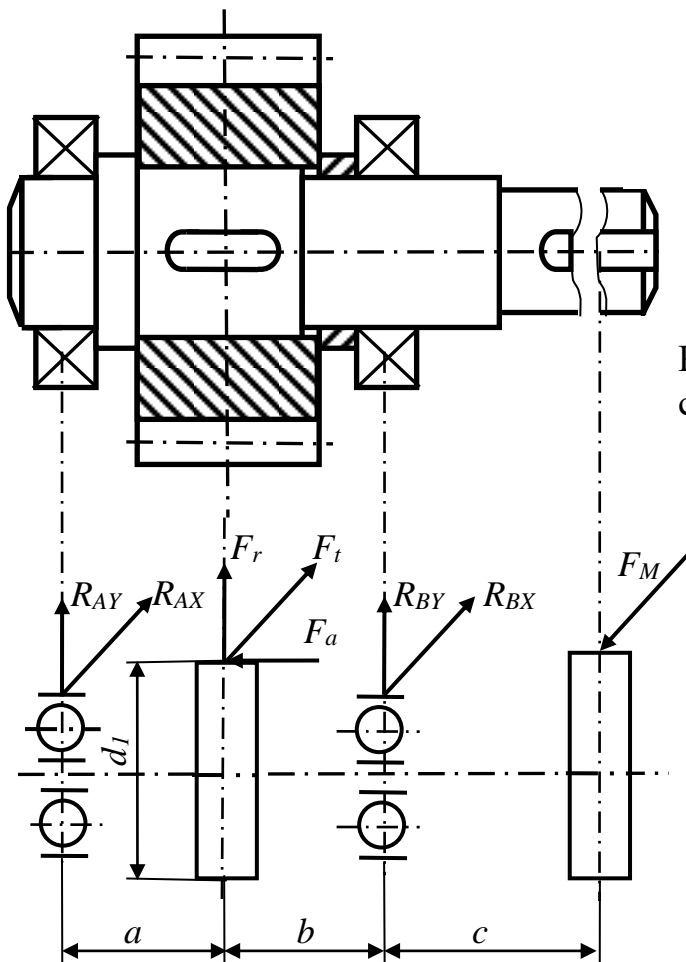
Эскиз и расчетная схема первичного вала редуктора.
